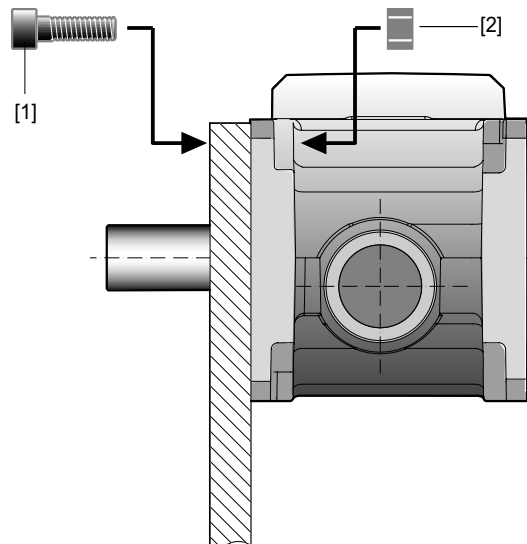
Монтаж конического редуктора BSF... на опорную конструкцию установки
